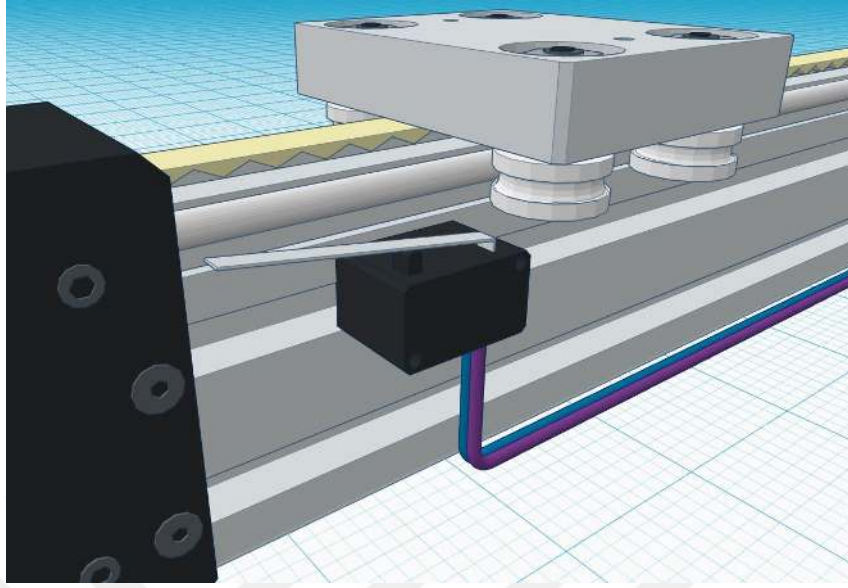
Motorun yüzey ve pistle bağlantısı
